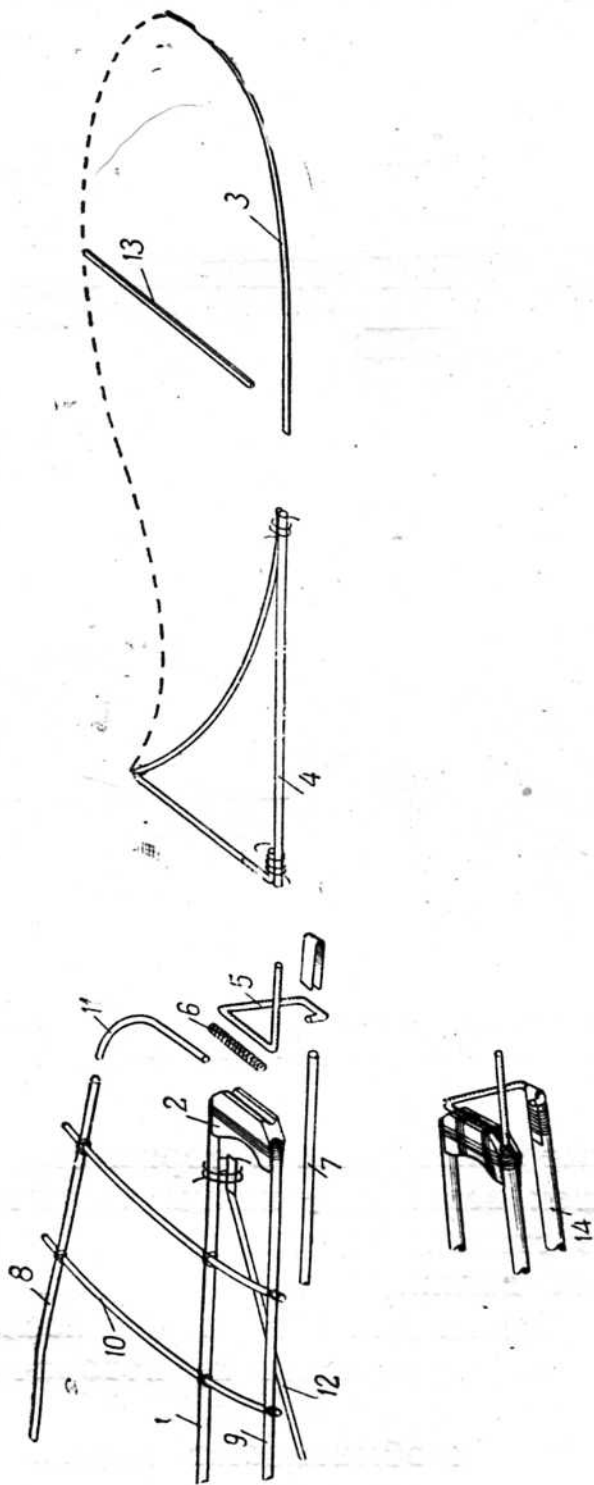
Сборка узлов, расположенных около двуручных качалок: 1 — лонжерон крыла; 2 — бобышка; 3 — законцовки машущих крылышек (бамбук); 4 — лонжерон машущих крылышек (соломка); 5 — качалка двуручная; 6 — подшипник качалки (спиральная пружинка); 7 — тяга-шатун; 8 — задняя кромка крыла; 9 — передняя кромка крыла; 10 — нервюра крыла; 11 — закругление крыла; 12 — подкос; 13 — нервюра машущего крылышка (кусочек расщепленной соломки); 14 — крепление двуручных качалки с подшипником в бобышке
